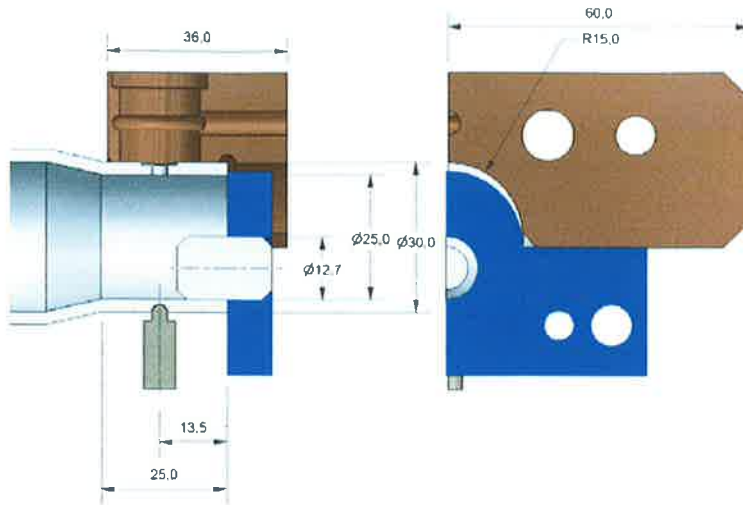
Dimensiones en mm de la posición de los componentes.
